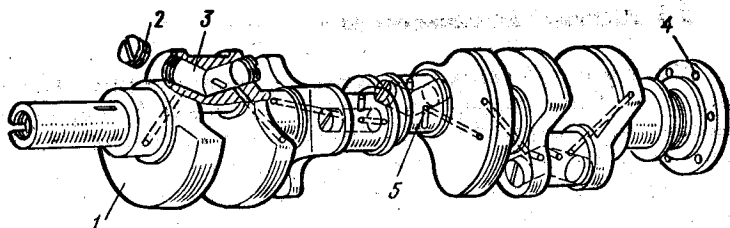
Колінчастий вал V-подібного 8-циліндрового двигуна ЗИЛ-130:
